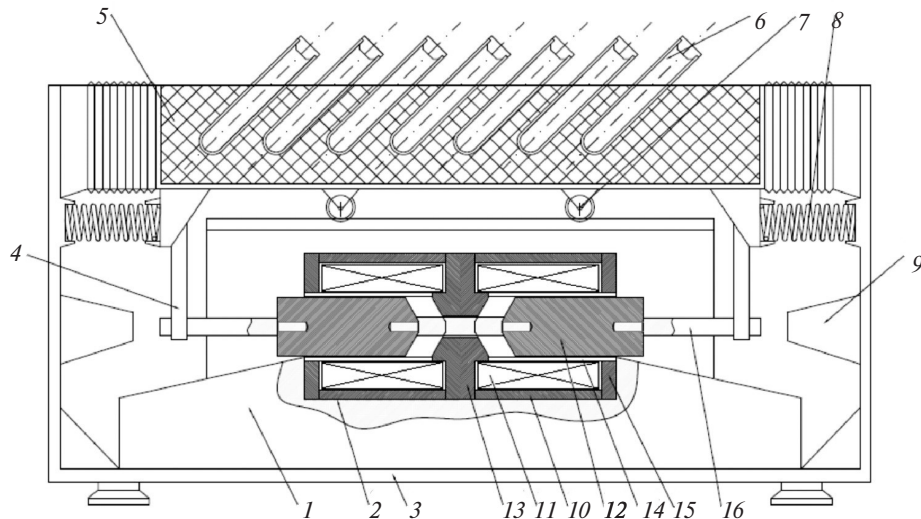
Лабораторный шейкер: 1 – станина; 2 – ЛЭМД; 3 – корпус; 4 – скоба; 5 – столик; 6 – пробирки со штативом; 7 – ролики; 8 – пружины; 9 – резиновые демпферы; 10 – магнитопровод; 11 – катушки; 12 – якорь (шток); 13 – полюс (стоп); 14 – немагнитная гильза; 15 – проходной фланец; 16 – рабочий орган (направляющий вал)
